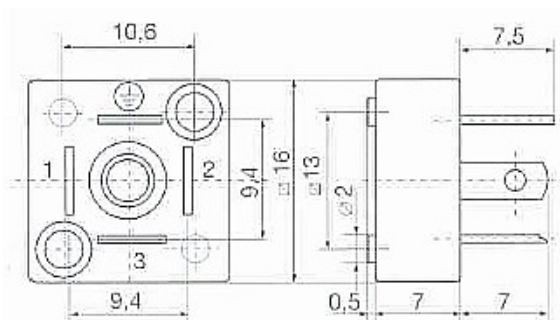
База для герморазъёма DIN 43650, форма С (соединитель электрический, промышленный стандарт) с тремя контактами плюс заземляющий контакт
